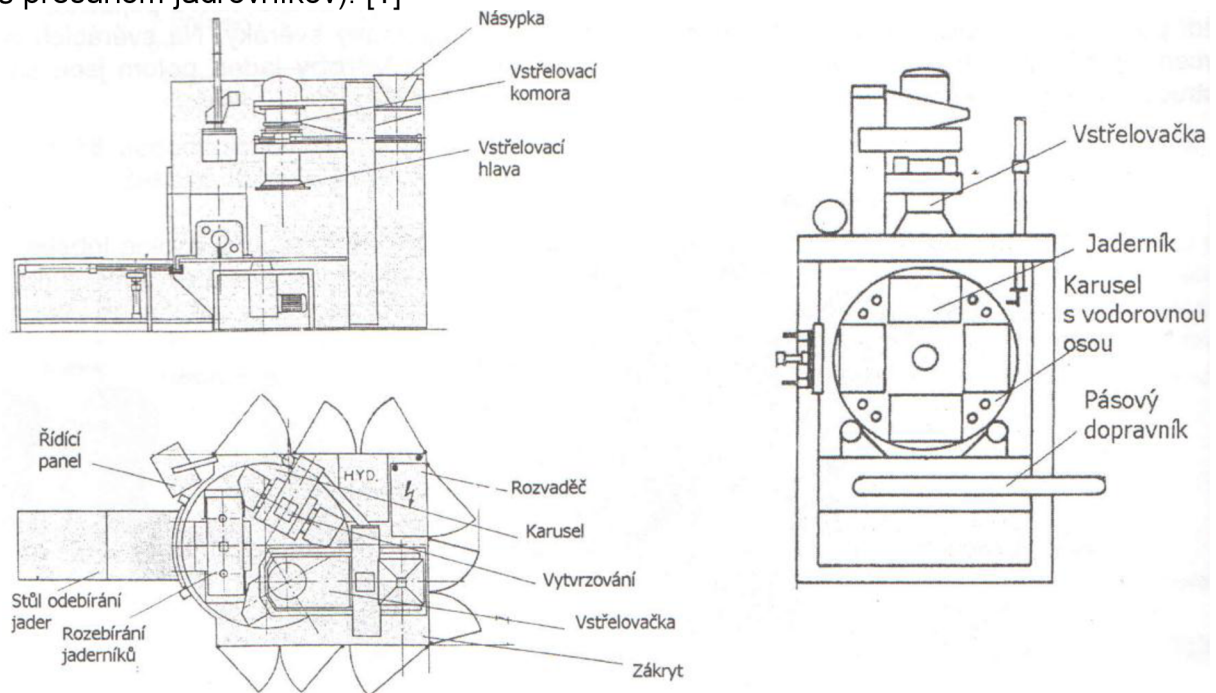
Univerzální vstřelovací CB stroj (Roperwerk HM) [1]
